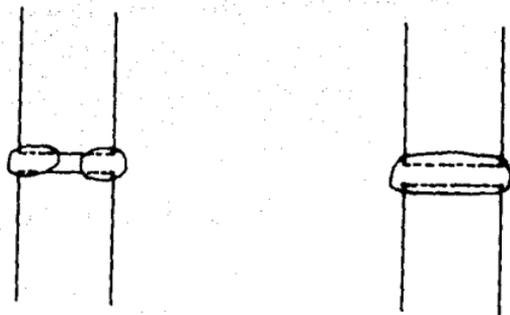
Soldadura Provicional o por Puntos.
